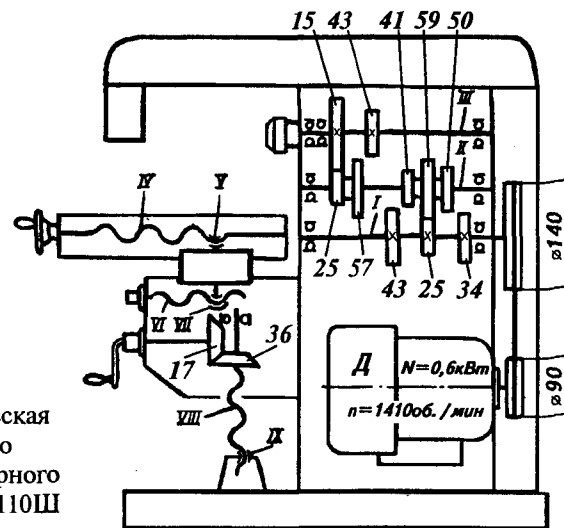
Кинематическая схема настольного горизонтально-фрезерного станка модели НГФ-110Ш
